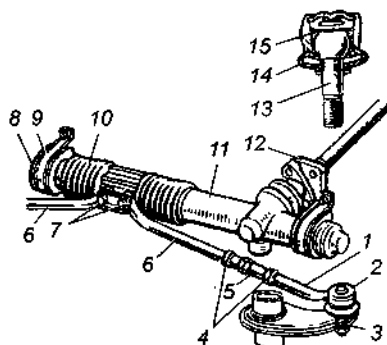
Проверка зазора шарниров рулевых тяг на переднеприводных автомобилях марки «ВАЗ»: 1 — наконечник рулевой тяги; 2 — шаровой шарнир наконечника; 3 — поворотный рычаг; 4 — гайка; 5 — регулировочная тяга; 6 — рулевые тяги; 7 — болты крепления рулевых тяг к рейке; 8 — опора рулевого механизма; 9 — опора рулевого механизма; 10 — гофрированный защитный чехол редуктора; 11 — картер редуктора; 12 — упругая муфта; 13 — палец шарового шарнира; 14 — защитный чехол шарового шарнира; 15 — вкладыш шарового пальца
